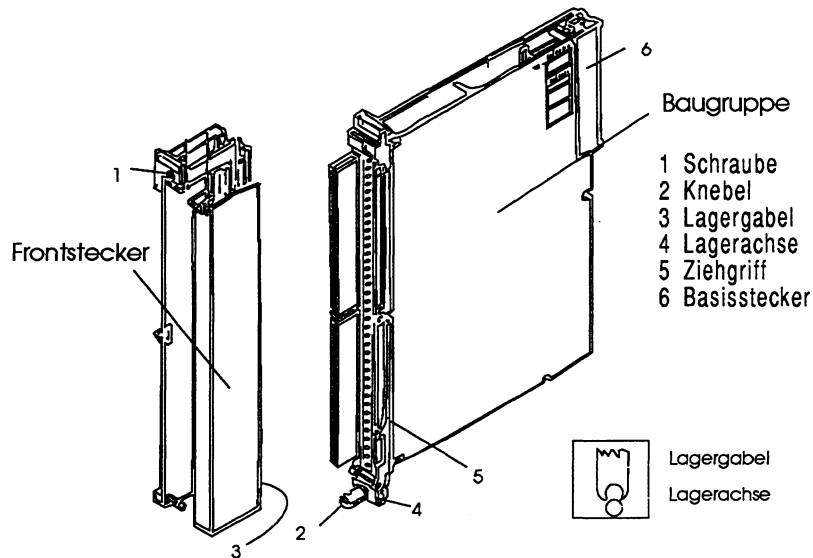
Baugruppe mit 20 mm Einbaubreite und Frontstecker mit Crimpkontakten
